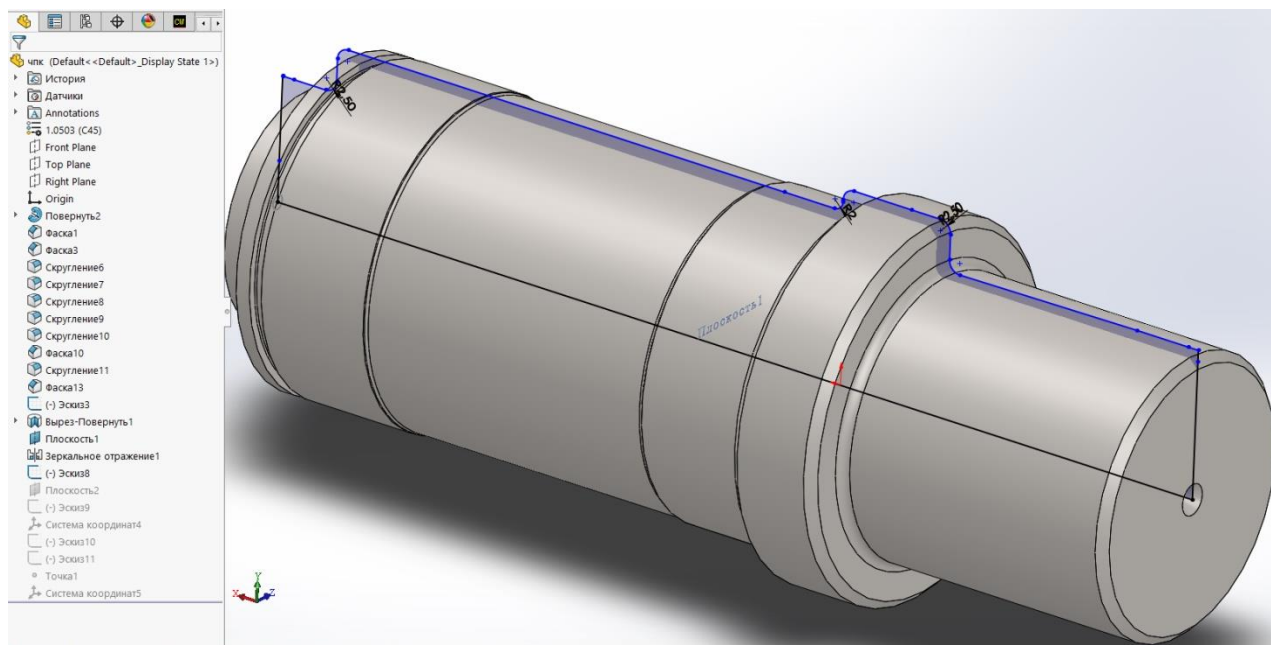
3D модель деталі та 2D ескіз заготовки
